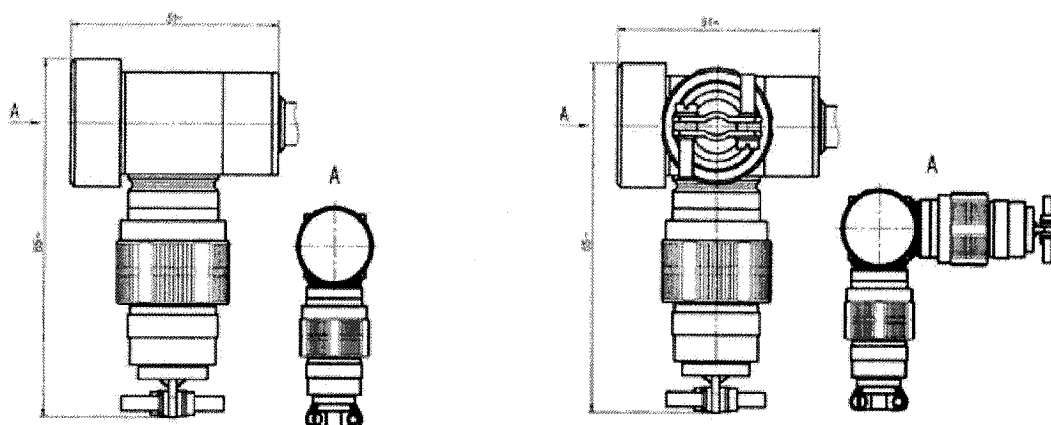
Кресленик зовнішньої частини ТХА-1090, ТХК-1090 з головою
